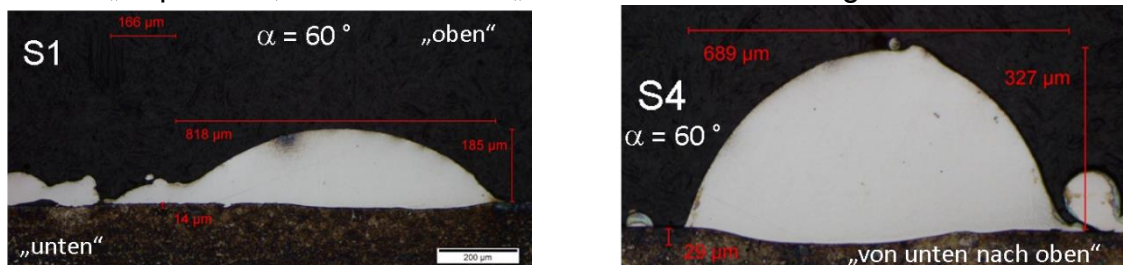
Querschliffe von Seite 1 (links) und Seite 4 (rechts) eines bei einem Neigungswinkel von 60° geschweißten Quadrats
